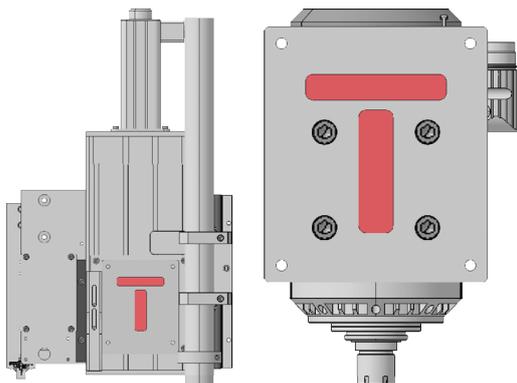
(A) AUFNAHME AN DER BEARBEITUNGSEINHEIT, (B) AUSSPARUNG AN DER SPINDELPLATTE (RÜCKANSICHT)
